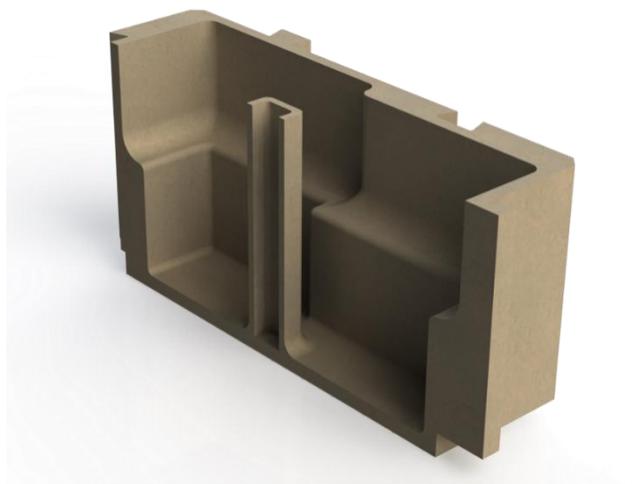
\_2 – Sección macetero de hormigón con cola de milano
